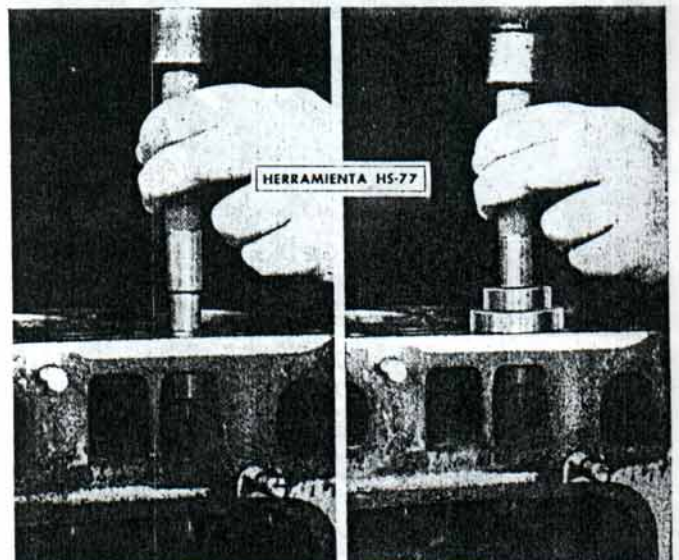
Extrayendo y colocando la guía de válvula, con el motor del vehículo desmontado.
